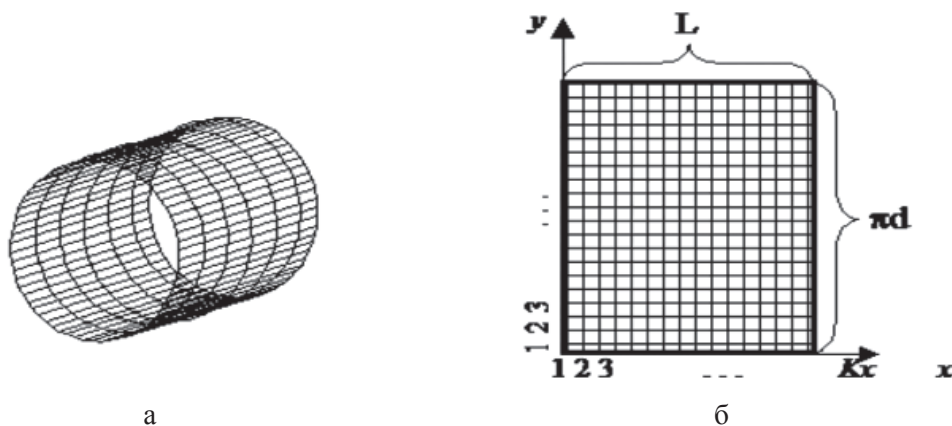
Интерполяция обрабатываемой поверхности: а – модель обрабатываемой поверхности; б – разработка модели обрабатываемой поверхности
